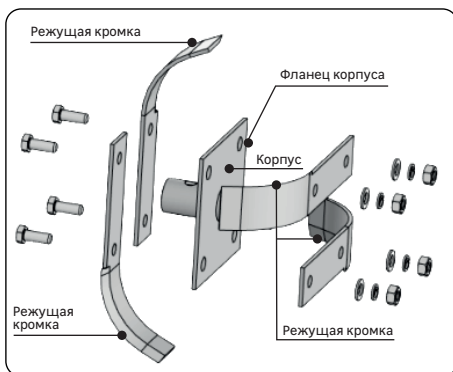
Схема установки культиваторов на редуктор мотокультиватора
